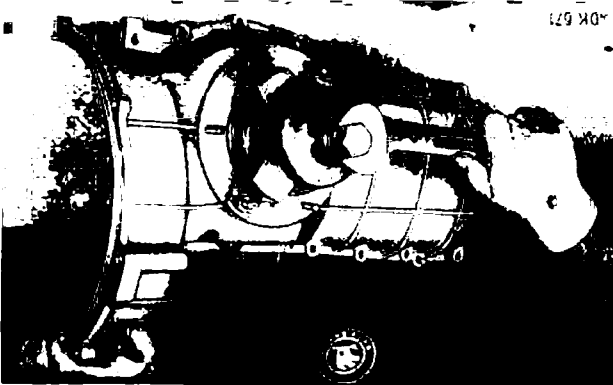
/2 Herauspressen der Kegelritzel-lageringe mit Hilfe der Montagevorrichtungen MP 5-107 und MP 5-108
